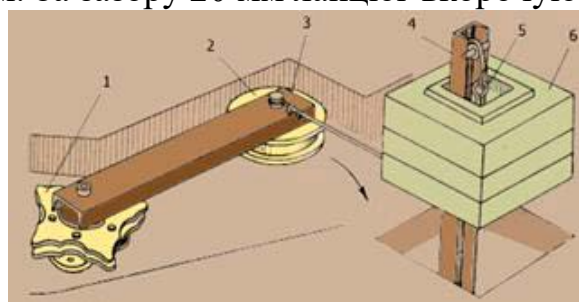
Автоматичний натяжний пристрій конвеєра КСГ-7:
